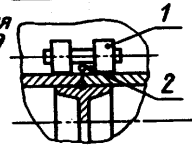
Схема сварки кольцевого стыка с наружным закреплением
